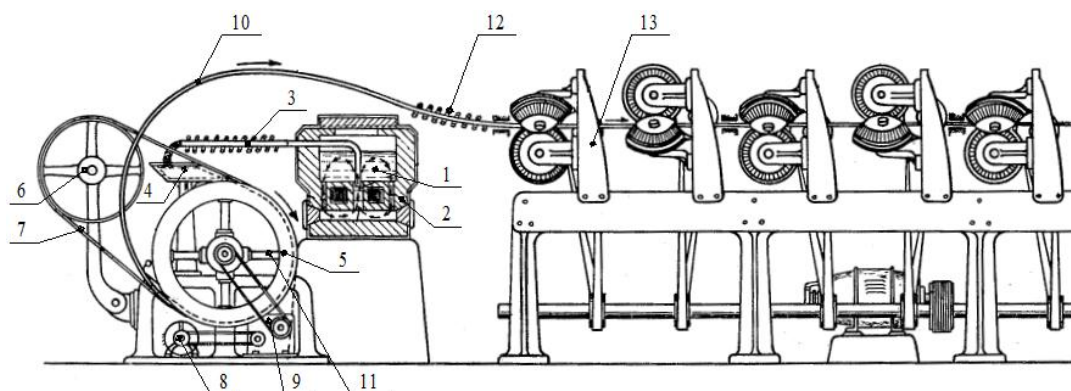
Принципиальная схема ЛПА конструкции PROPERZI: 1 – расплав меди; 2 – индукционная печь; 3 – огнеупорная труба; 4 – разливочный контейнер; 5 – литейное колесо; 6 – натяжное колесо; 7 – лента; 8 – двигатель; 9 – система передаточных механизмов; 10 – непрерывно-литая заготовка; 11 – спицы; 12 – проводки; 13 – прокатный стан
